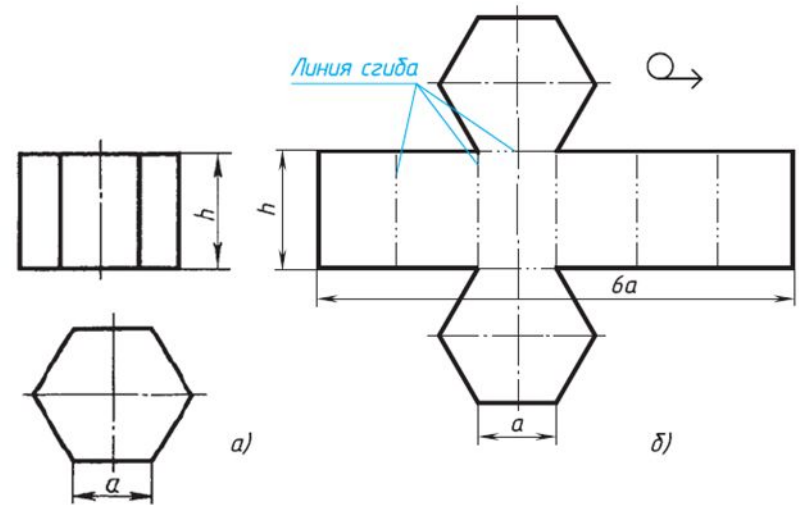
Построение чертежа развертки поверхностей призмы: *a* — два вида; *б* — развертка поверхностей
